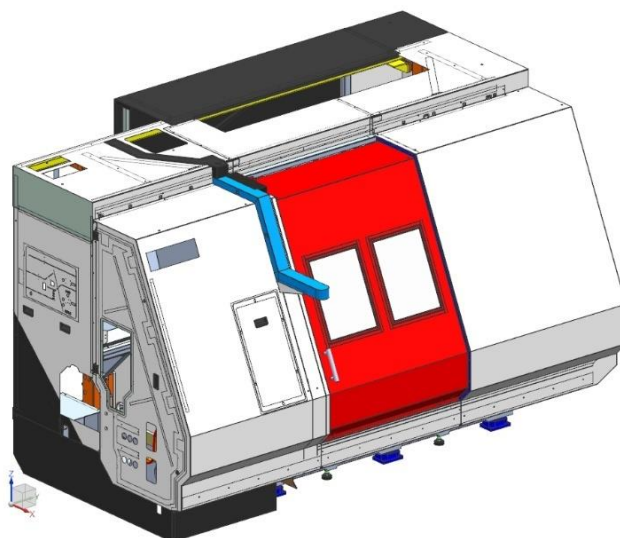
Ukázka projektu Run MyRobot/Machining v STEP 7
